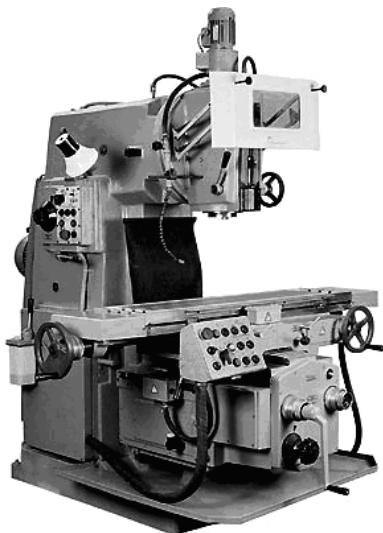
Внешний вид вертикально-фрезерного станка 6Р13
